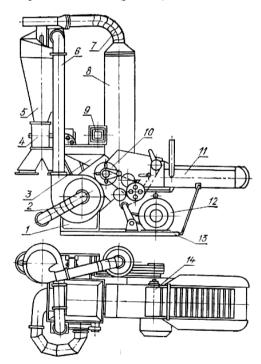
Универсальная дробилка кормов КДУ-2А:
